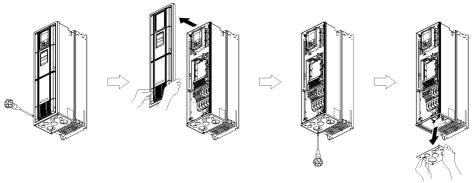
Extracción de la placa frontal y de la placa del cableado (FRN37AQ1M-4□)
